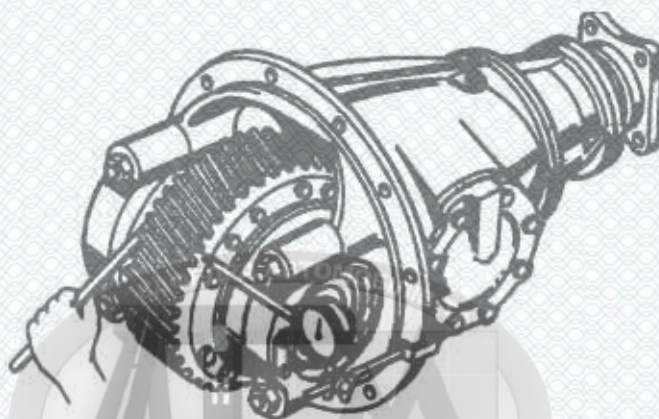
Перевірка осьового зазору в підшипниках диференціала за допомогою індикатора [10]
